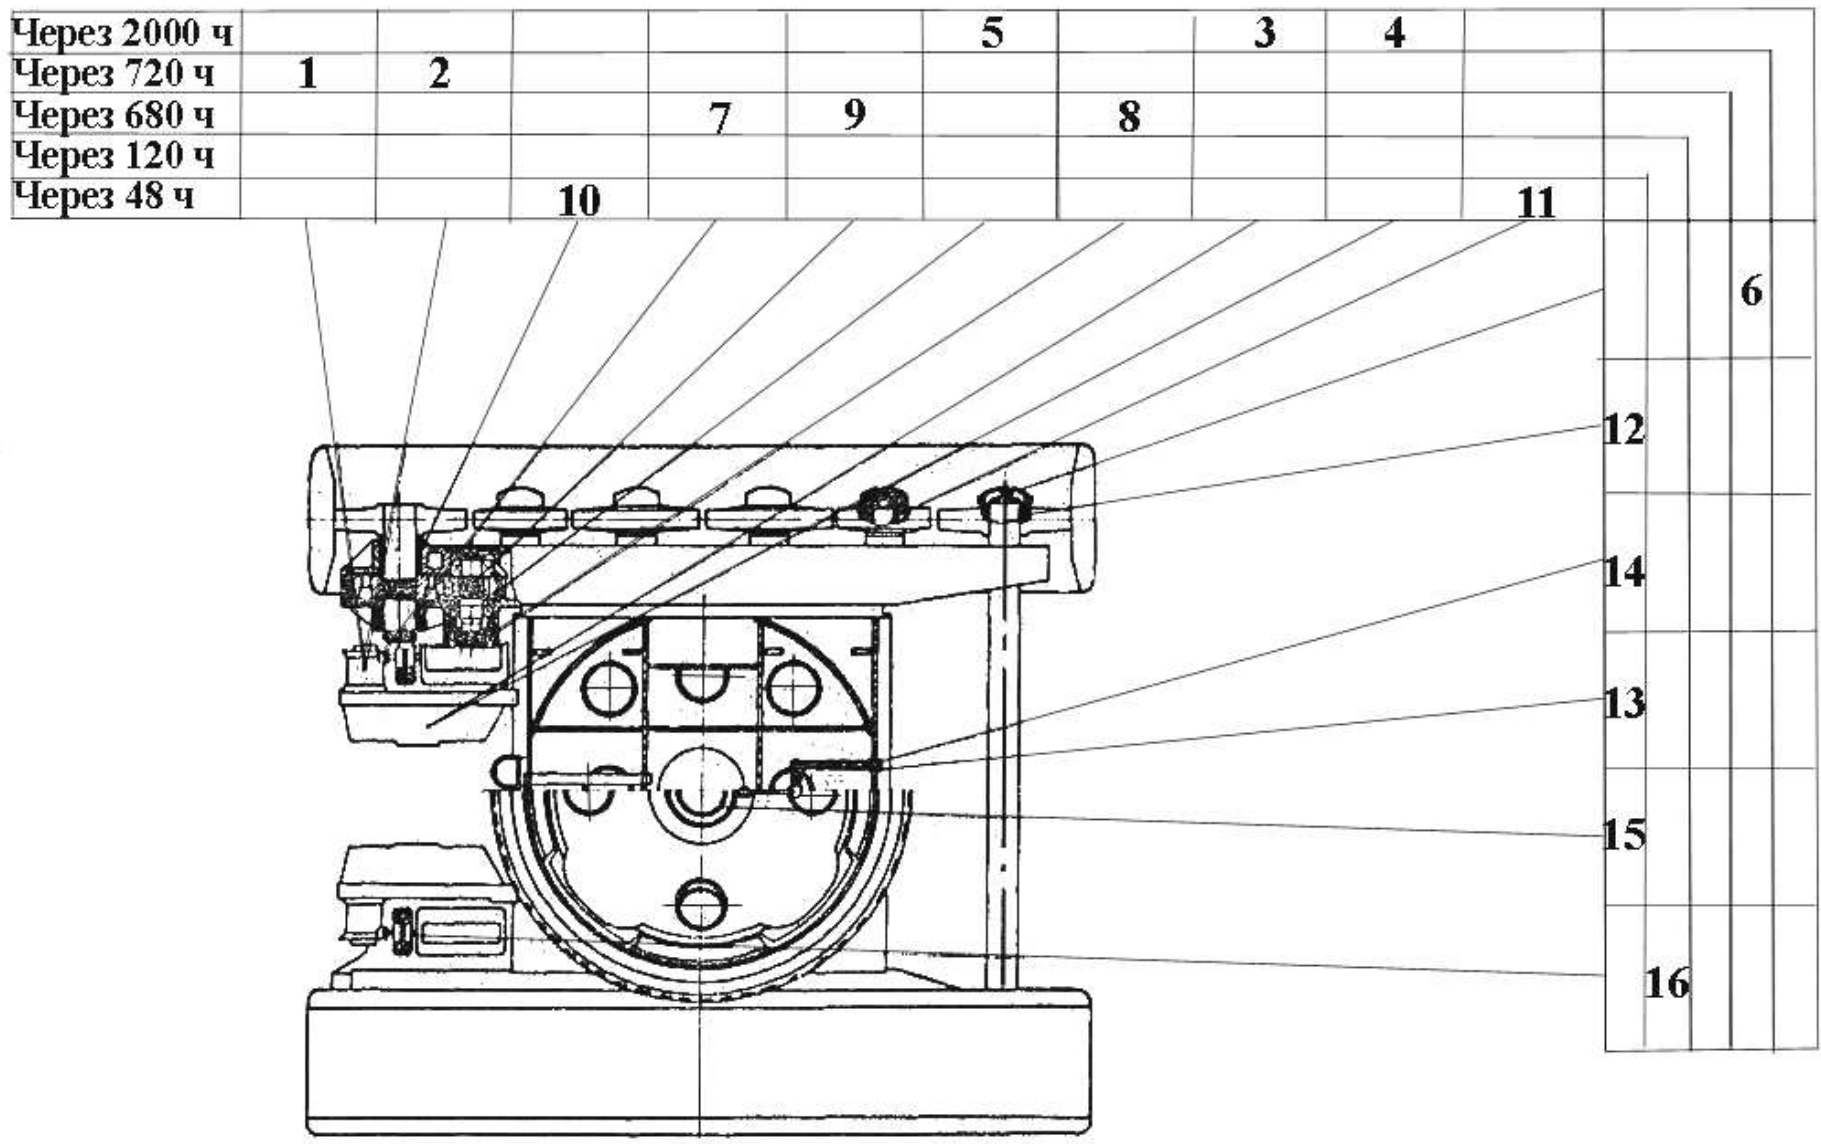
Схема смазки механизмов ходовой тележки экскаватора ЭКГ-10
